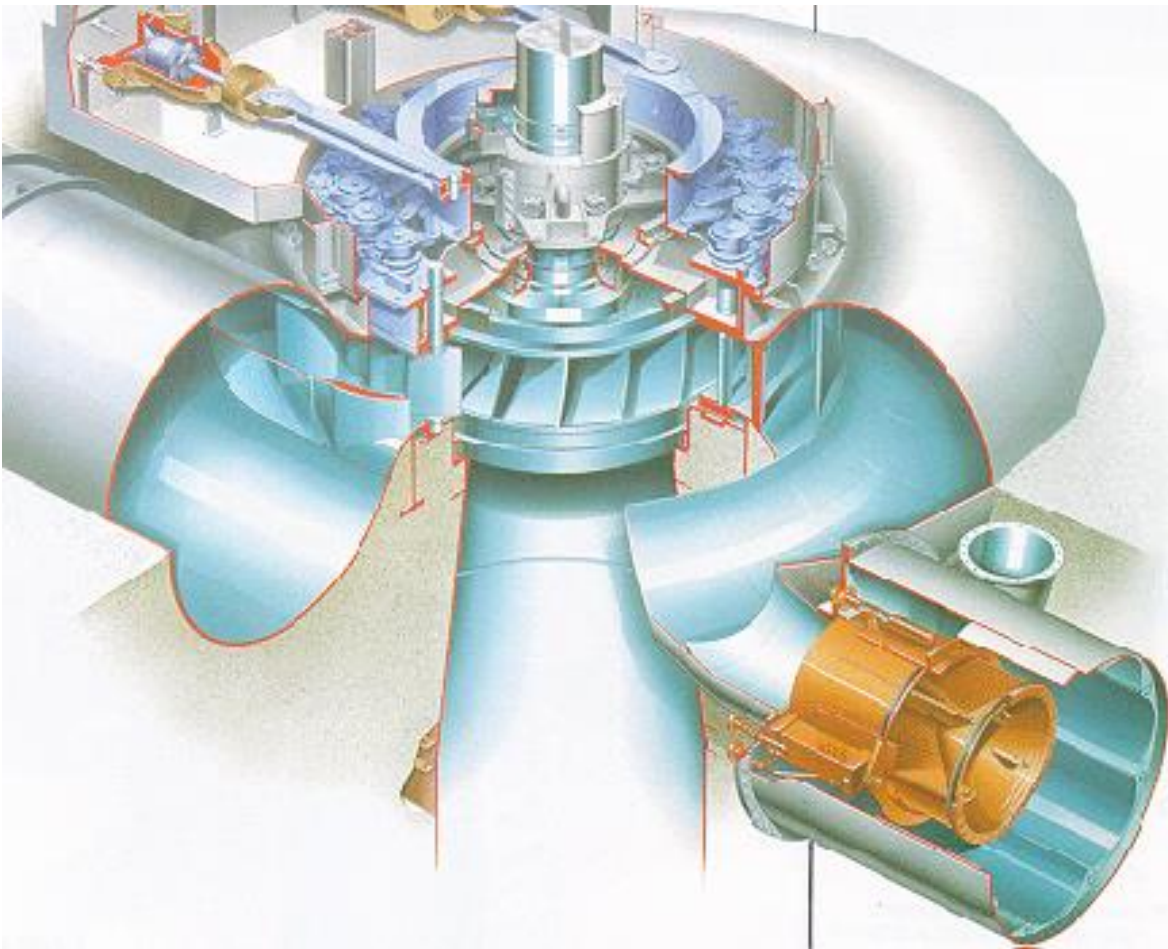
Turbina Francis. Fuente: Tecnología turbinas Francis.
